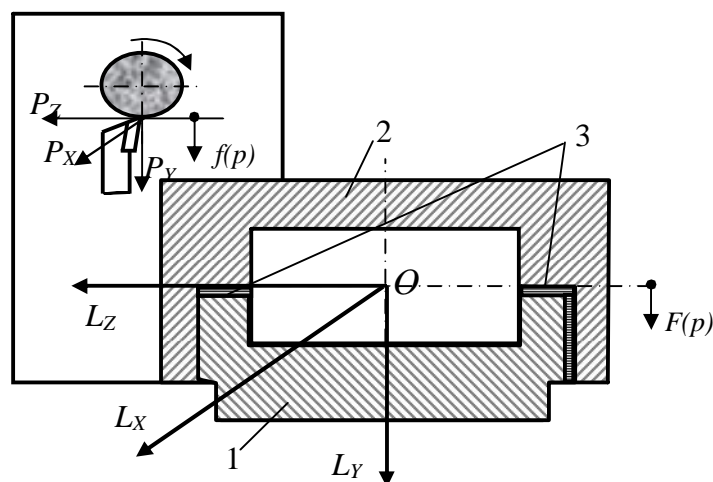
Схема стику «направляючі каретки – горизонтальні направляючі станини»: 1 – станина верстату; 2 – каретка револьверного супорту; 3 – стик
